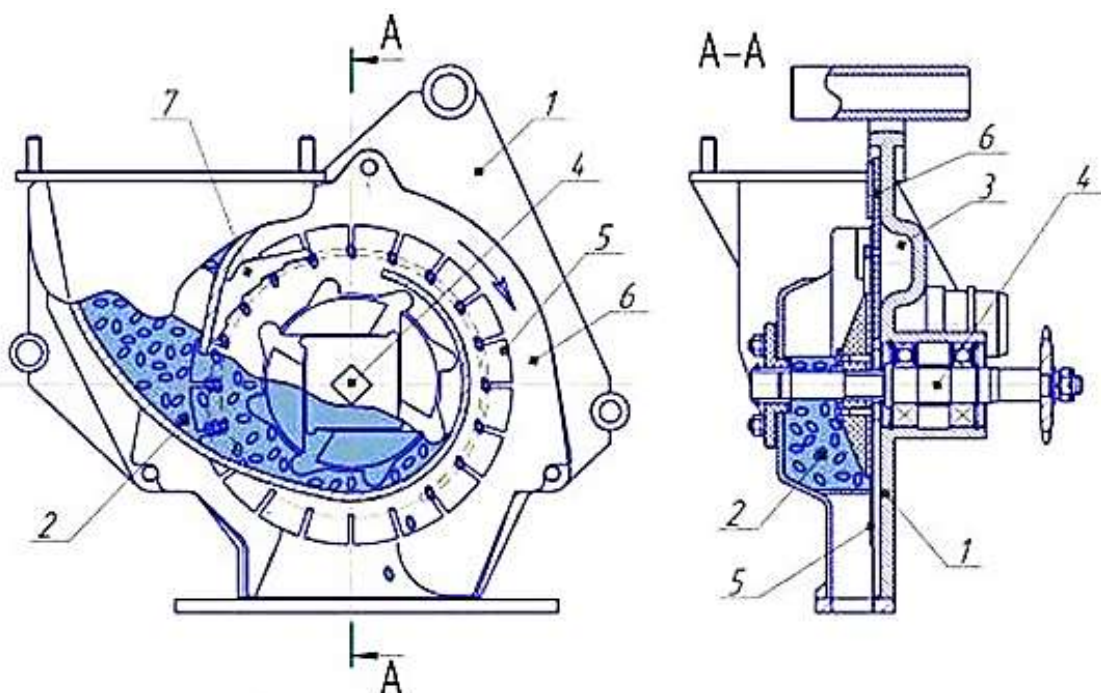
Схема высевающего аппарата предложенной конструкции
